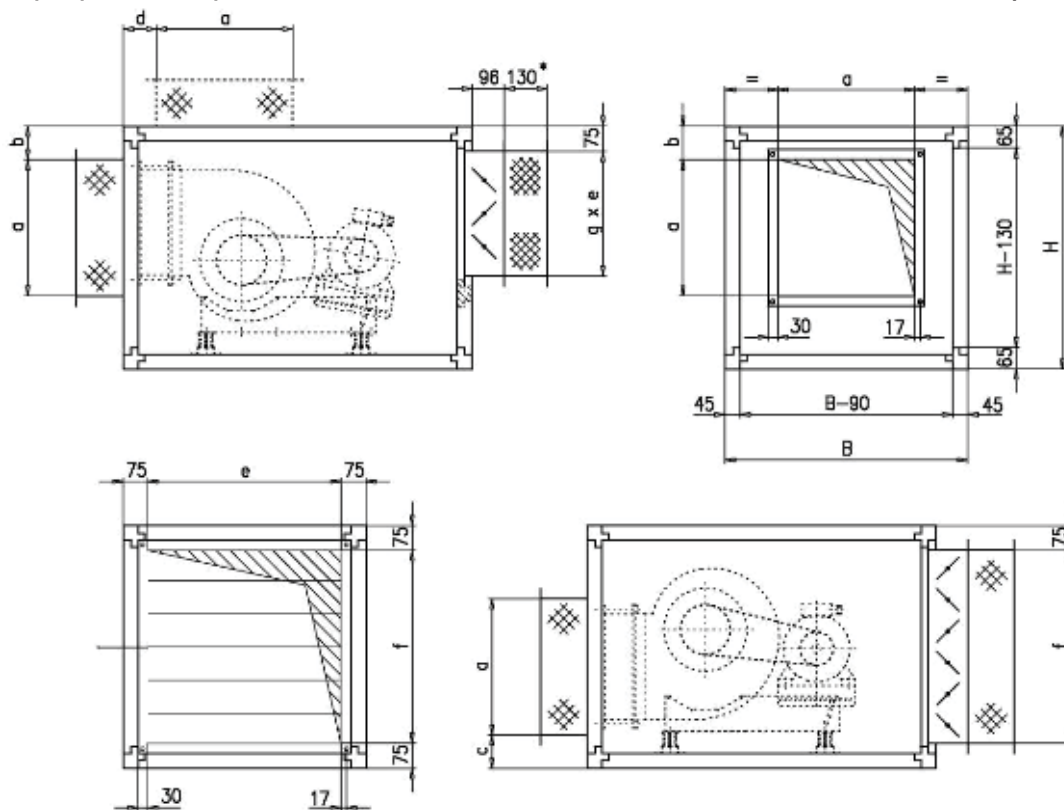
Габаритные и присоединительные размеры установок S40...Q(R), S60... Q(R)
